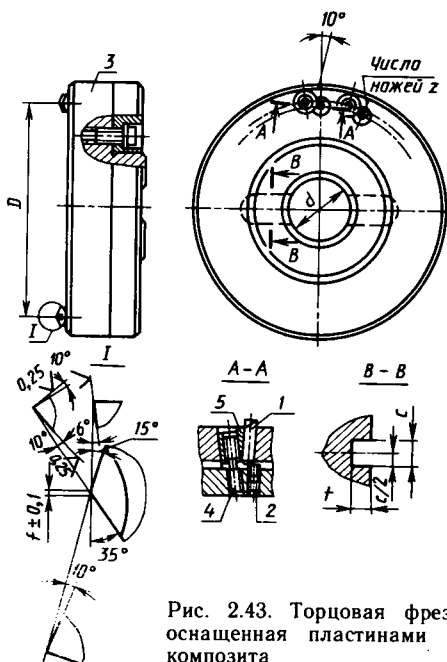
Торцовая фреза, оснащенная пластинами из композита
